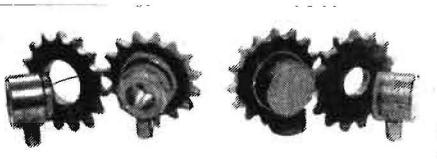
Kettenrad; links mit durchgesteckter Nabe CO₂-geschweißt, rechts stumpf-reibgeschweißt
